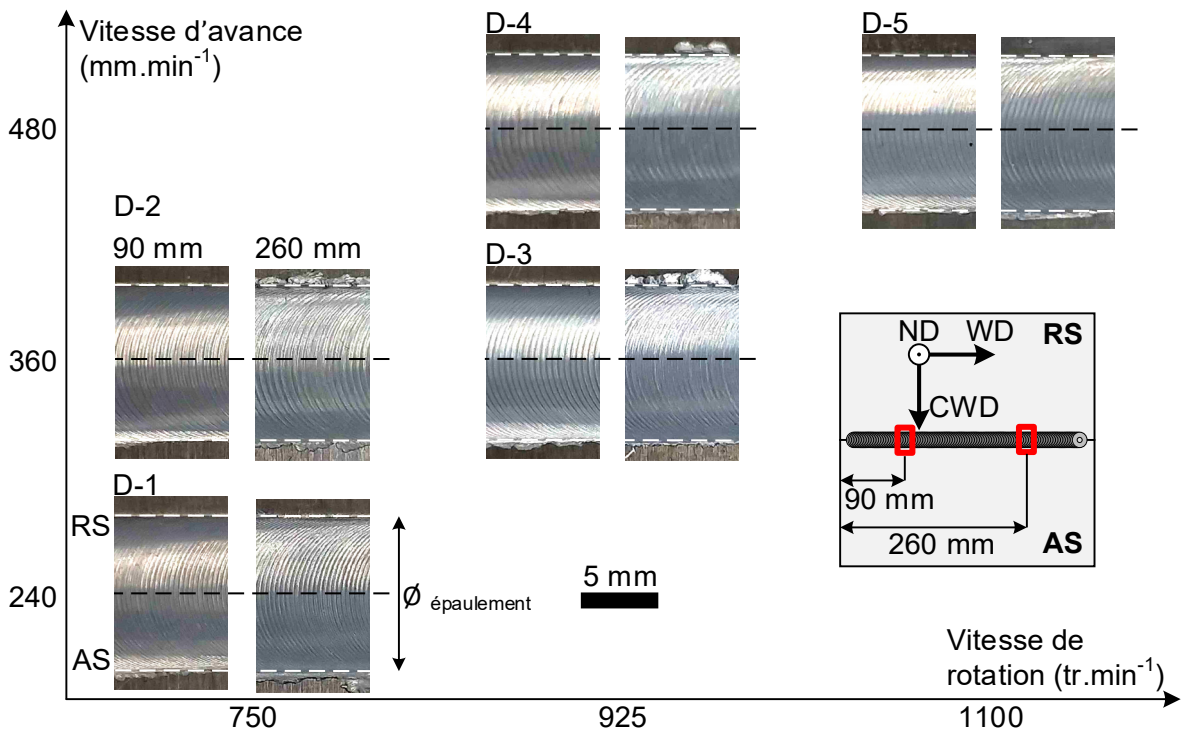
Matrice des états de surface des cordons de soudure en début de soudure (gauche) et en fin de soudure (droite).
